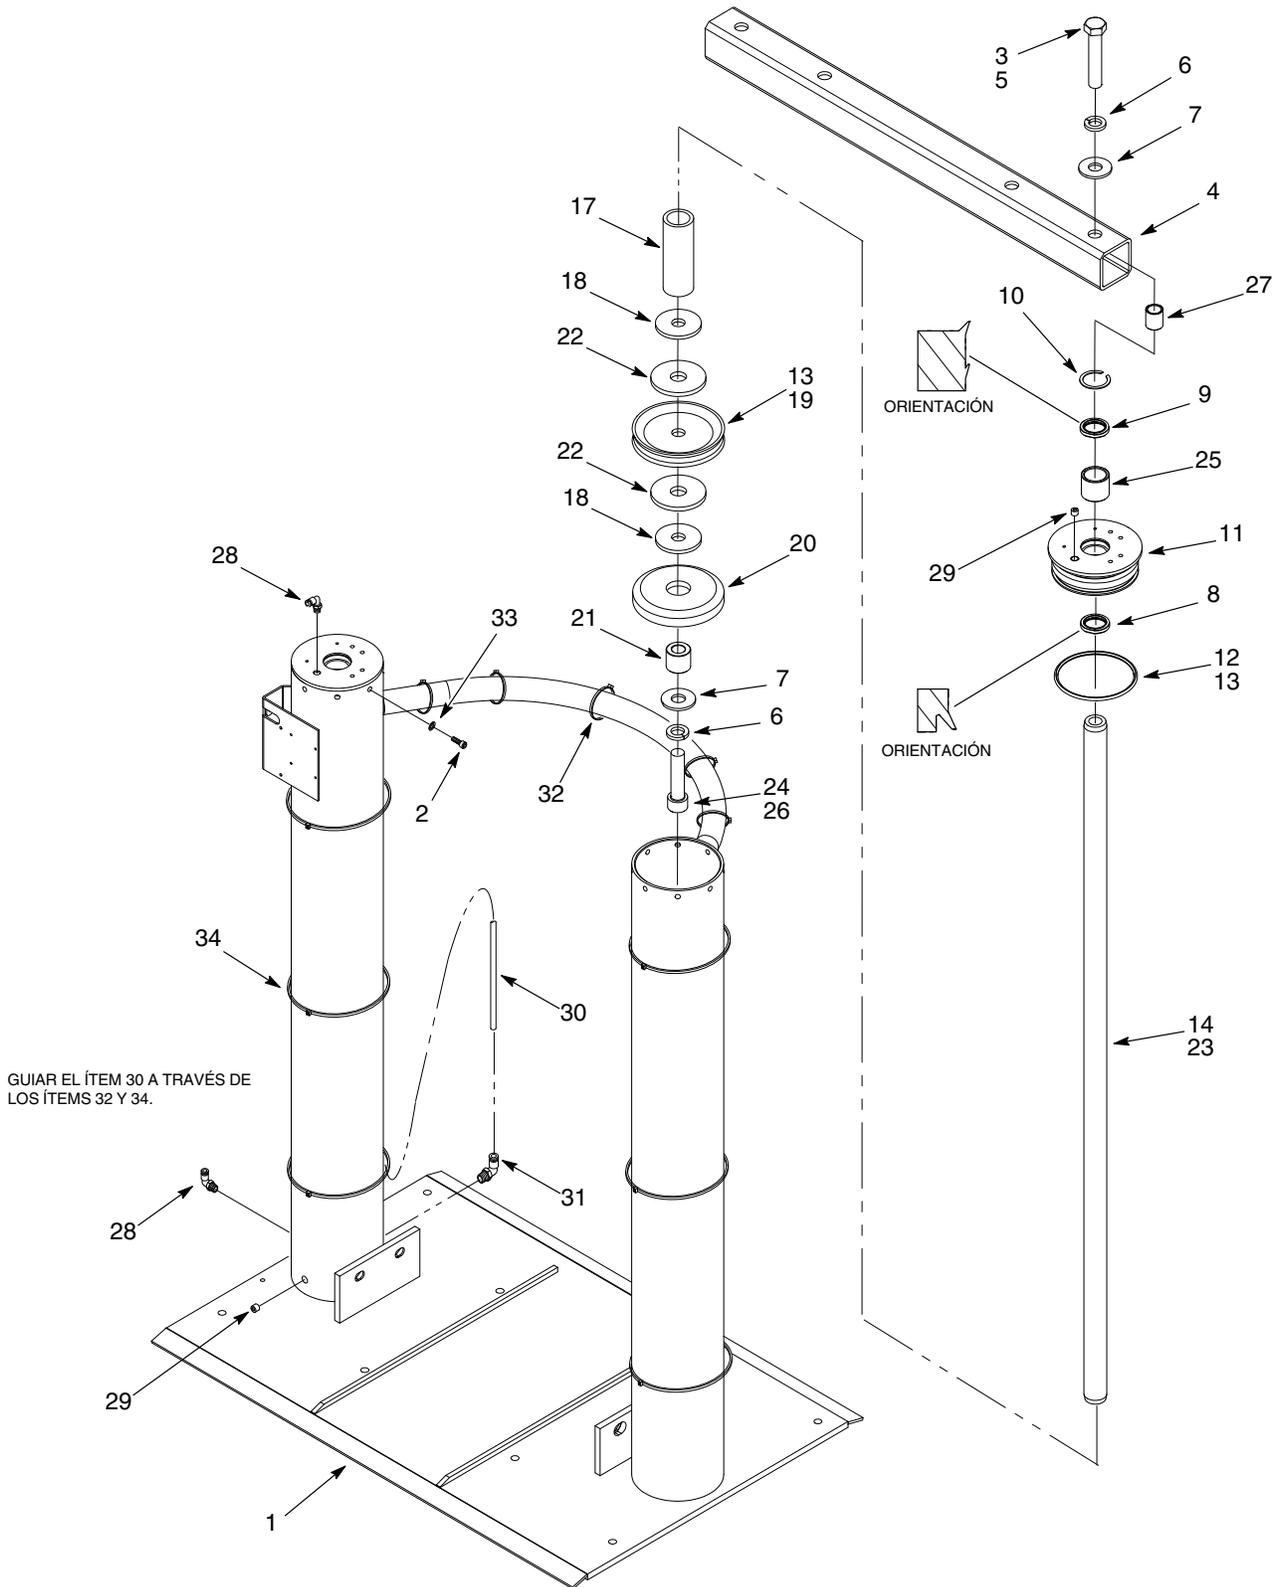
Piezas del soporte de la carretilla del tambor de 55 galones
